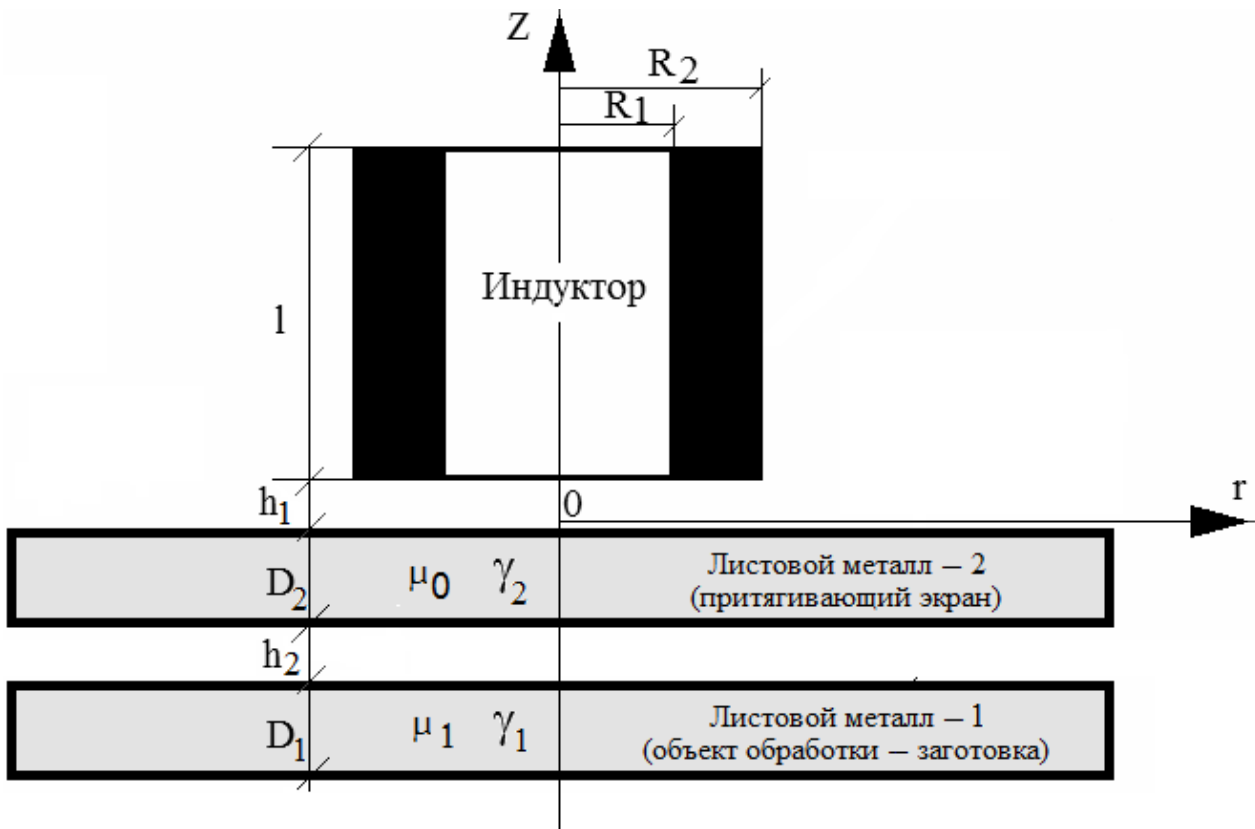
Модель индукторной системы с длинным цилиндрическим соленоидом – индуктором, на торце которого расположены тонкостенные листовые немагнитный экран и магнитная заготовка
